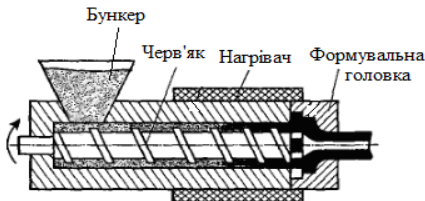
Схема черв'ячного екструдера для формування труб
